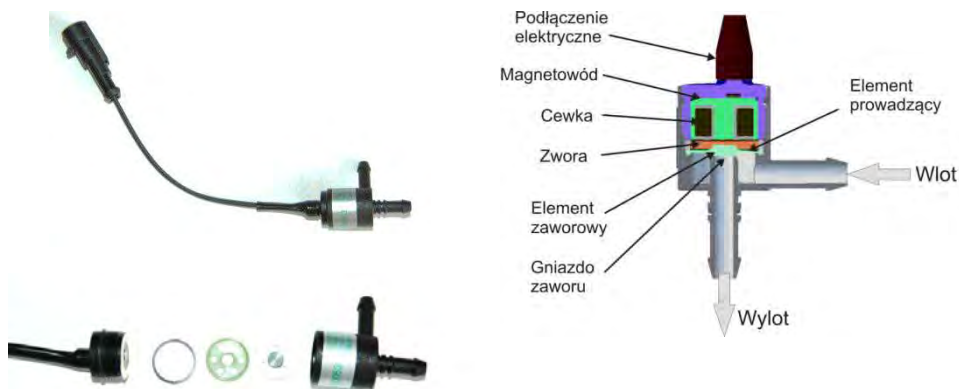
Konstrukcja wtryskiwacza PlaniJet
